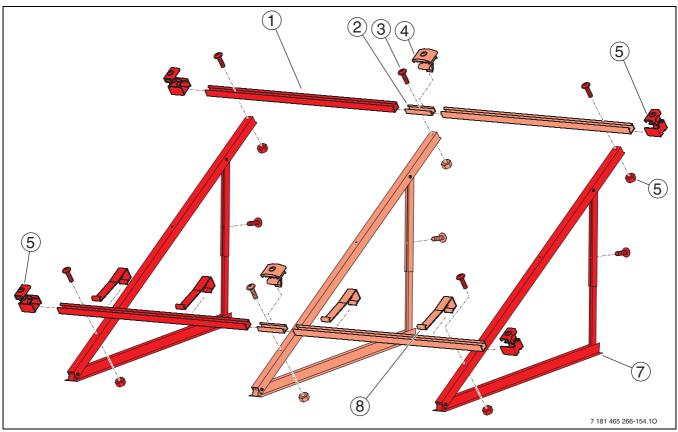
Grundmontage-Set und Erweiterungs-Set Flachdach
